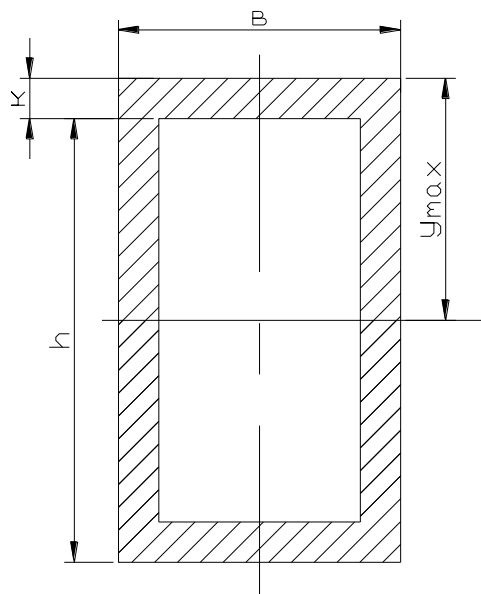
Форма поперечного перерізу зварного з'єднання
